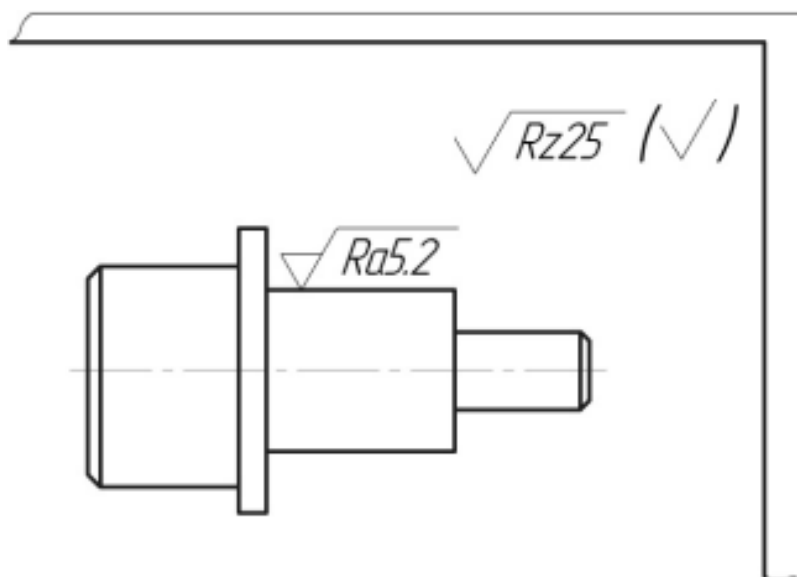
Указание шероховатости, одинаковой для части поверхности изделия
